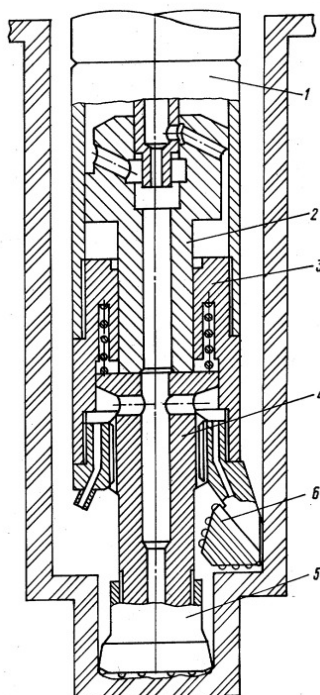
Комбинированный буровой инструмент, реализующий идею крупного скола: 1-пневмоударник; 2 – поршень; 3- букса; 4 – хвостовик; 5 - штыревая коронка; 6 - шарошка бурильной головки
